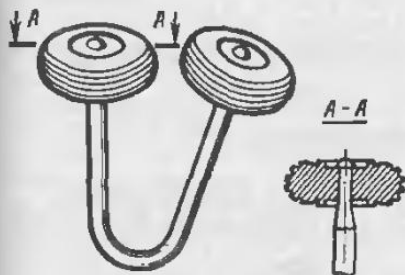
Образец закрепления колес из алюминиевых сплавов для цветного анодирования
